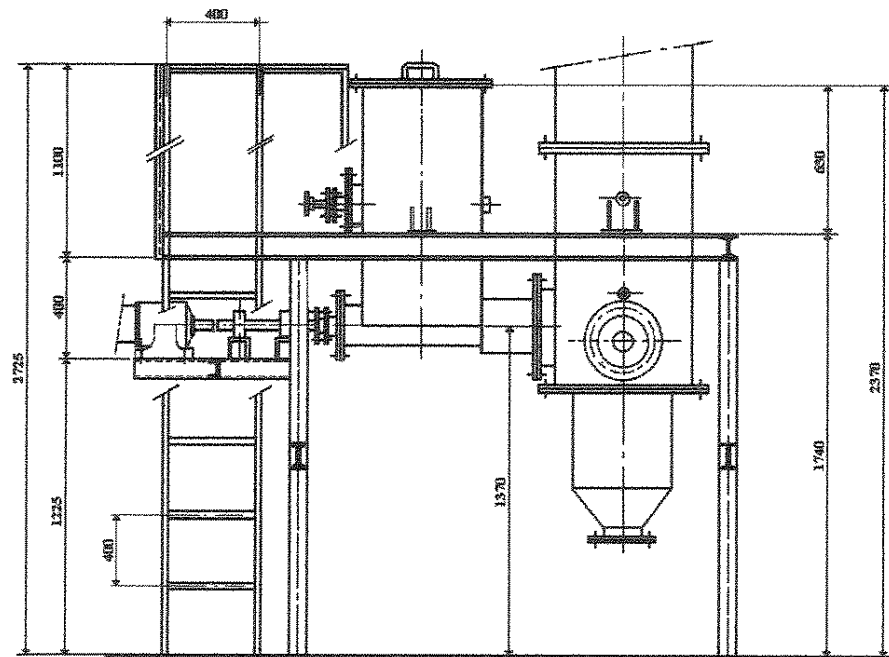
Estrutura de montagem do sistema de gaseificação
